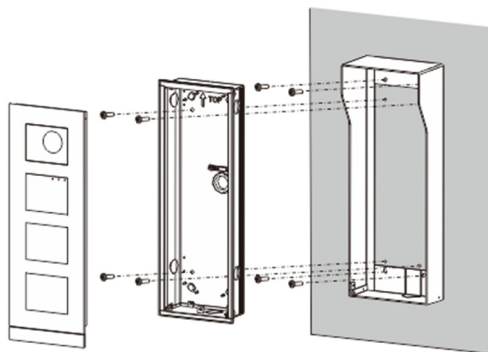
Montaggio a parete con copertura di protezione contro la pioggia
